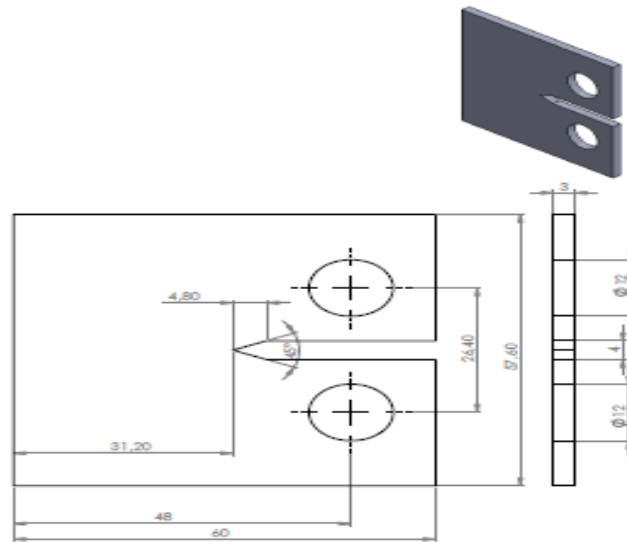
Géométrie et dimensions des éprouvettes CT utilisées.
